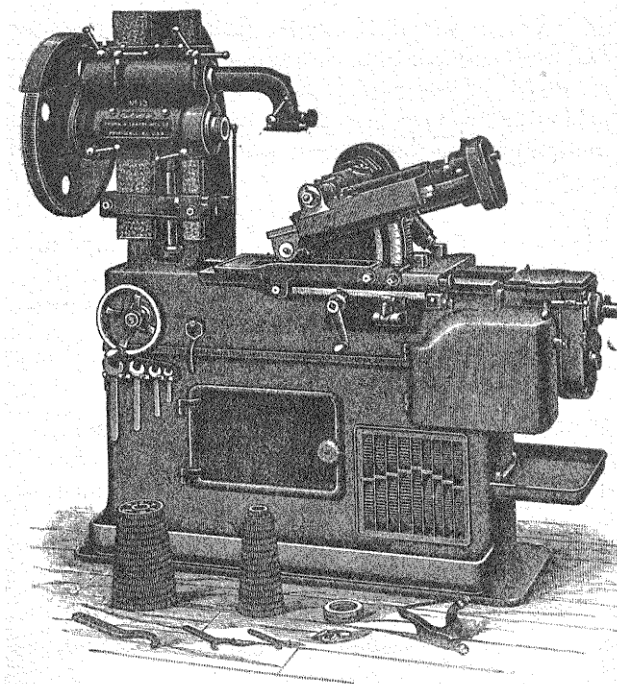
Machine automatique à tailler les engrenages droits et coniques Brown et Sharpe.
